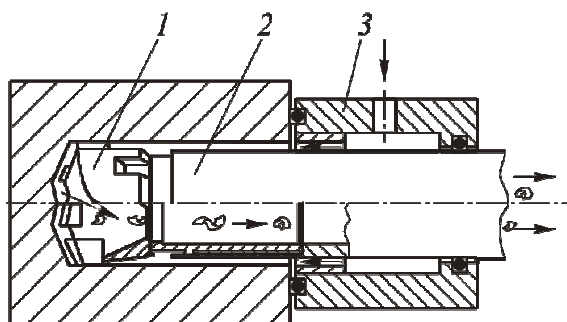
Схема обработки глубокого отверстия сверлом БТА:
